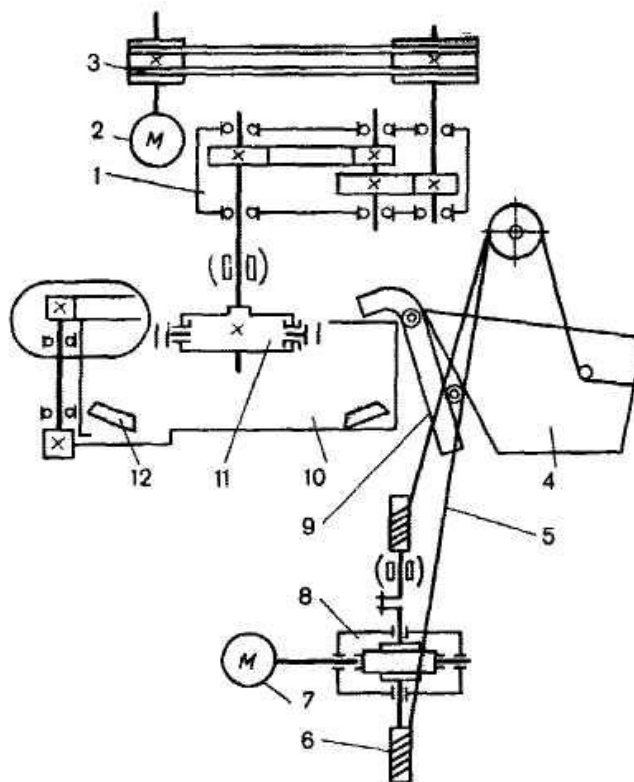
Кинематическая схема смесителя СБ-141:
